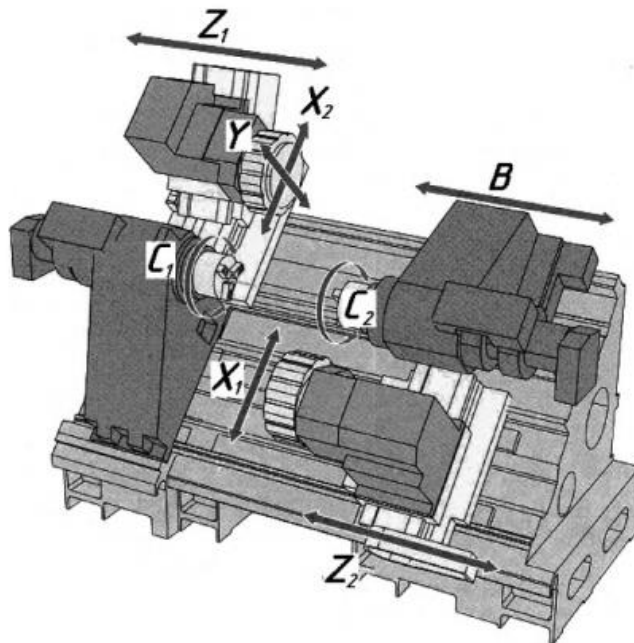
Положення вісей токарного верстата з ЧПУ з контршпинделем і двома револьверними головками
